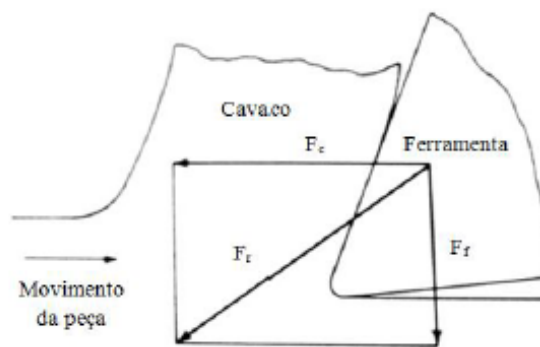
Componentes da força de usinagem (Adaptado de Boothroyd e Knight (1989)).
